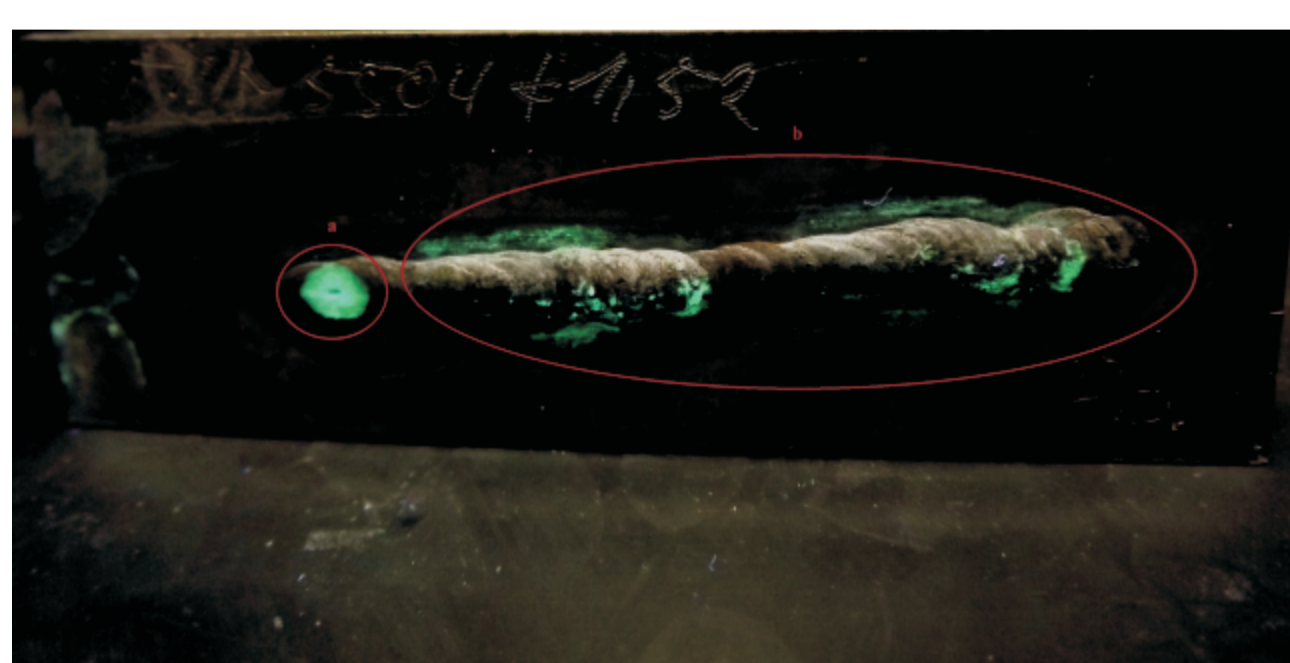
Próbkę nr 8 z warstwą napawaną wykonaną ze stopu Inconel 718. Fig. 4. Welding layer sample no. 8 made of Inconel 718
